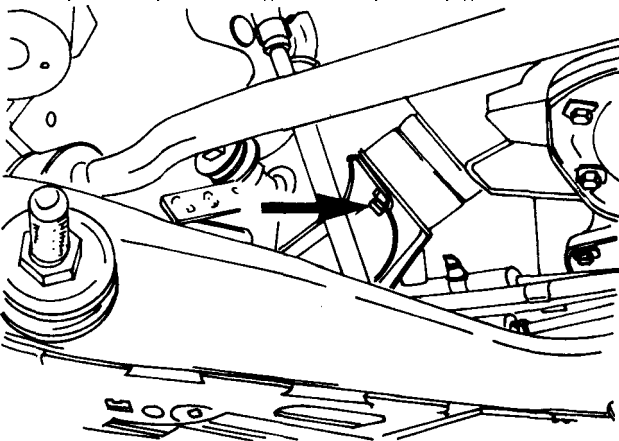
Стрелка указывает гайку подушки подвески двигателя.
